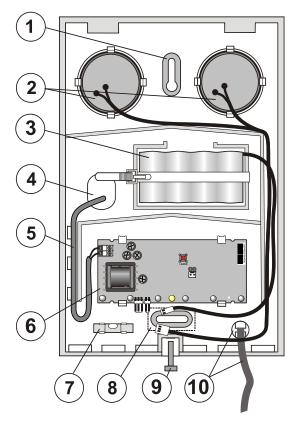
buraco de montagem; 2 – sirene piezo; 3 – bateria NiCd; 4 – buraco para o cabo; 5 – cabo de alimentação; 6 – PCB; 7 – nível de bolha; 8 – buraco de montagem com detecção de tamper; 9 – parafuso frontal; 10 – fio com clipe para conectar a tampa frontal para fácil instalação
